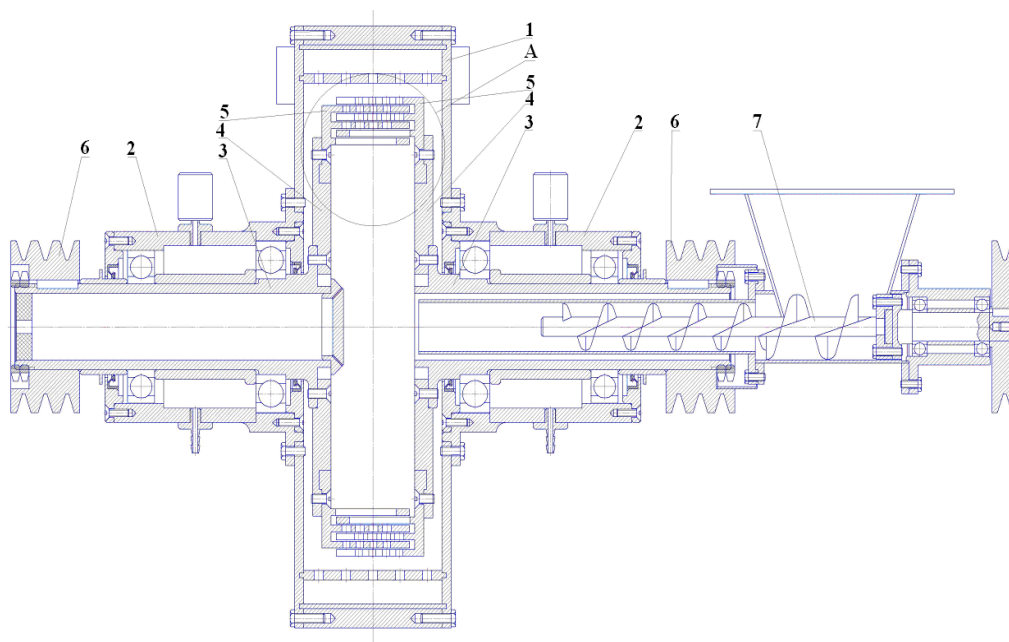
Вид загальний дезінтегратора: 1 – помольна камера, 2 – корпус шпинделя; 3 – опора, 4 – диск ротора; 5 – робочі кільця; 6 – шків; 7 – завантажувальний шнек.
